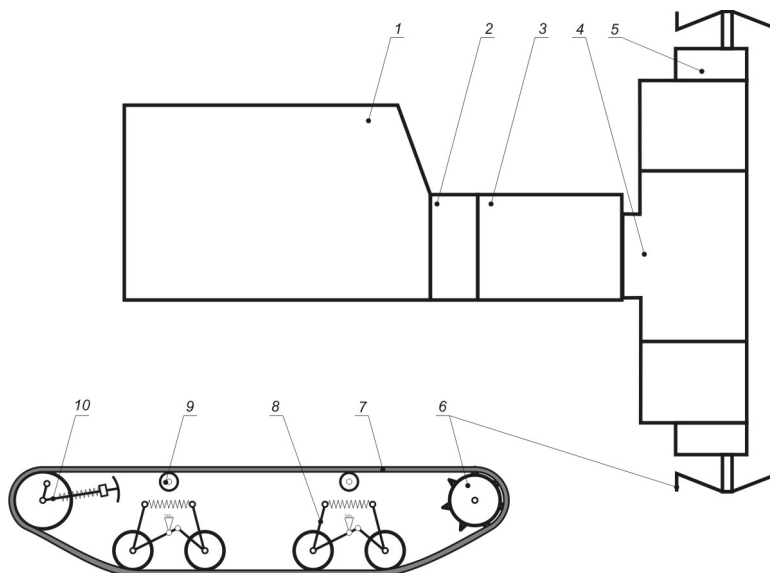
Кинематическая схема гусеничной машины: 1 – двигатель внутреннего сгорания (ДВС); 2 – сцепление; 3 – коробка перемены передач; 4 – задний мост с главной передачей и дифференциальным механизмом; 5 – бортовой редуктор; 6 – ведущая звездочка; 7 – гусеничная цепь; 8 – каретка; 9 – поддерживающий ролик; 10 – натяжной механизм
